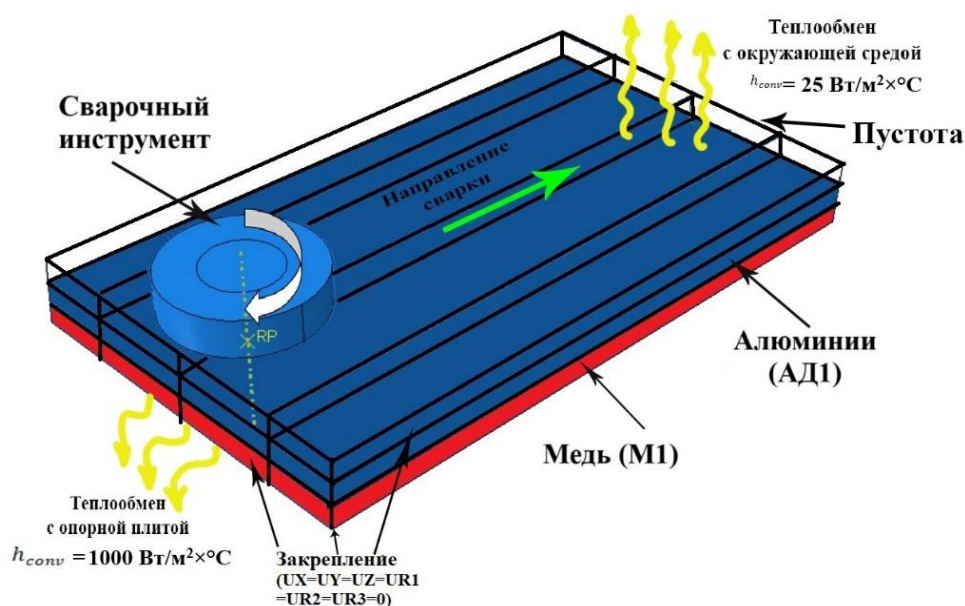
Сборка лагранжевого инструмента и эйлеровой заготовки
